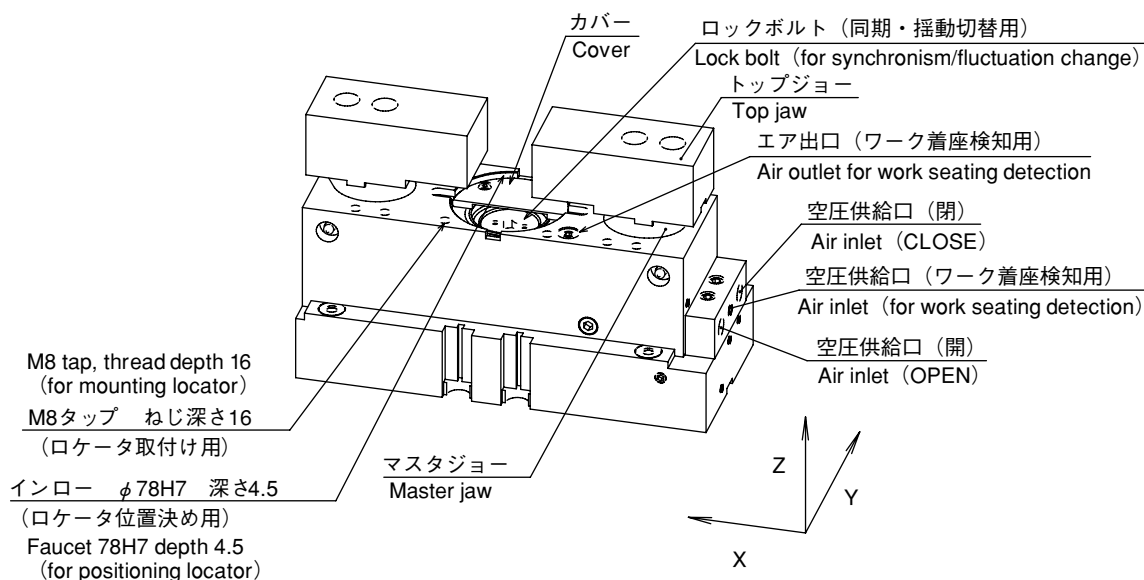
治具モジュール外観図 Appearance of Jig Module
